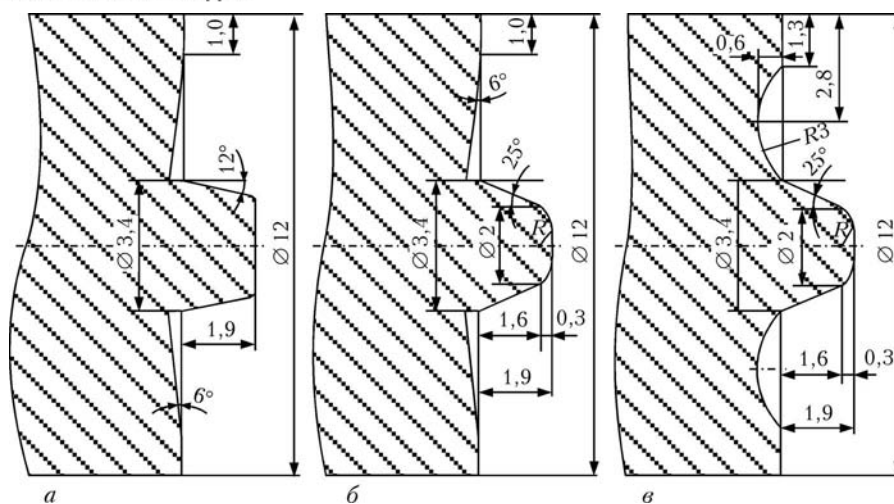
Эскизы рабочих частей инструментов с конической (а, б) и полусферической (в) канавками на рабочей поверхности бурта и различной формой наконечников для СТП алюминиевых сплавов толщиной 2 мм
